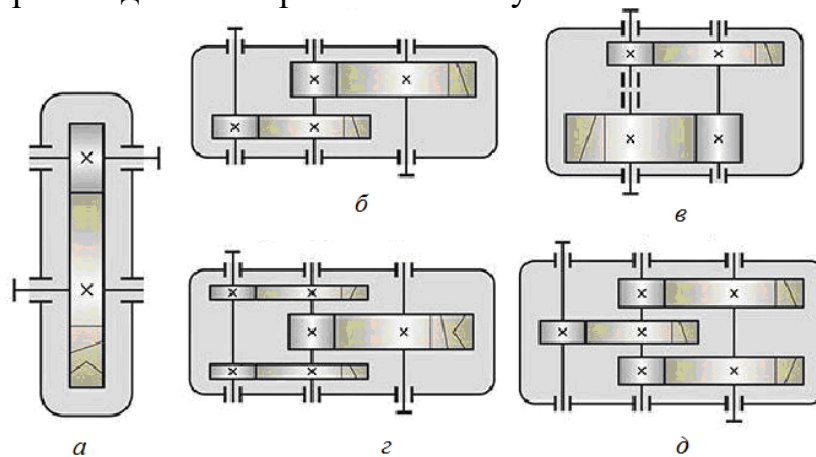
Цилиндрические редукторы: а – одноступенчатый, б–д – двухступенчатые
